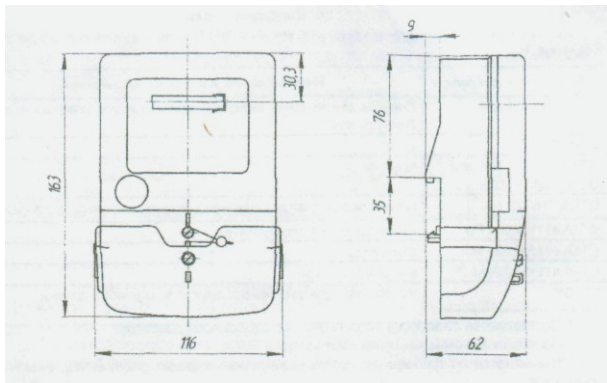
Общий вид счетчика в корпусе типа P1
